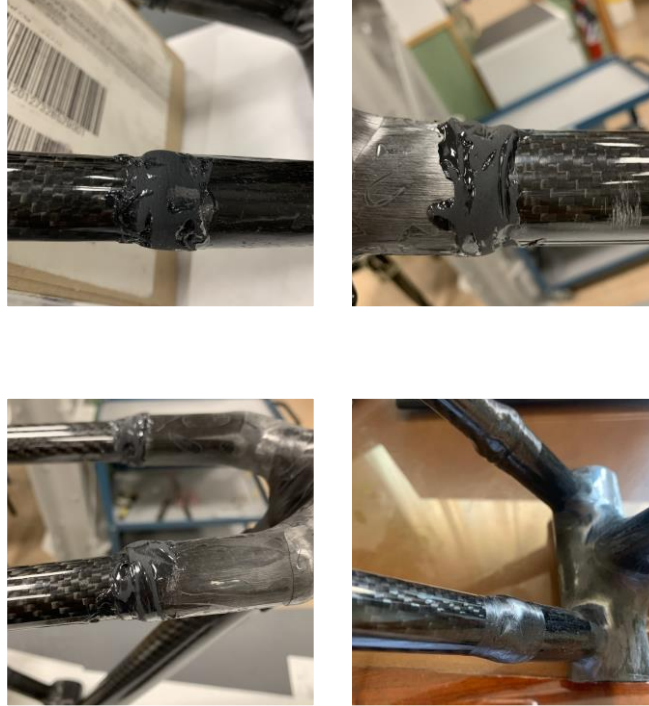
Lijado de excedente de adhesivo y uso de preimpregnado
